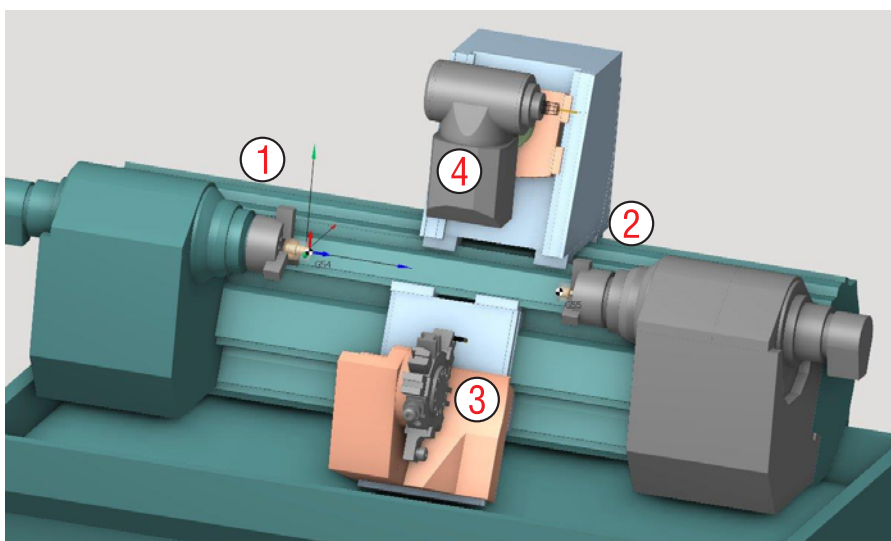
Токарно-фрезерный многозадачный станок.
